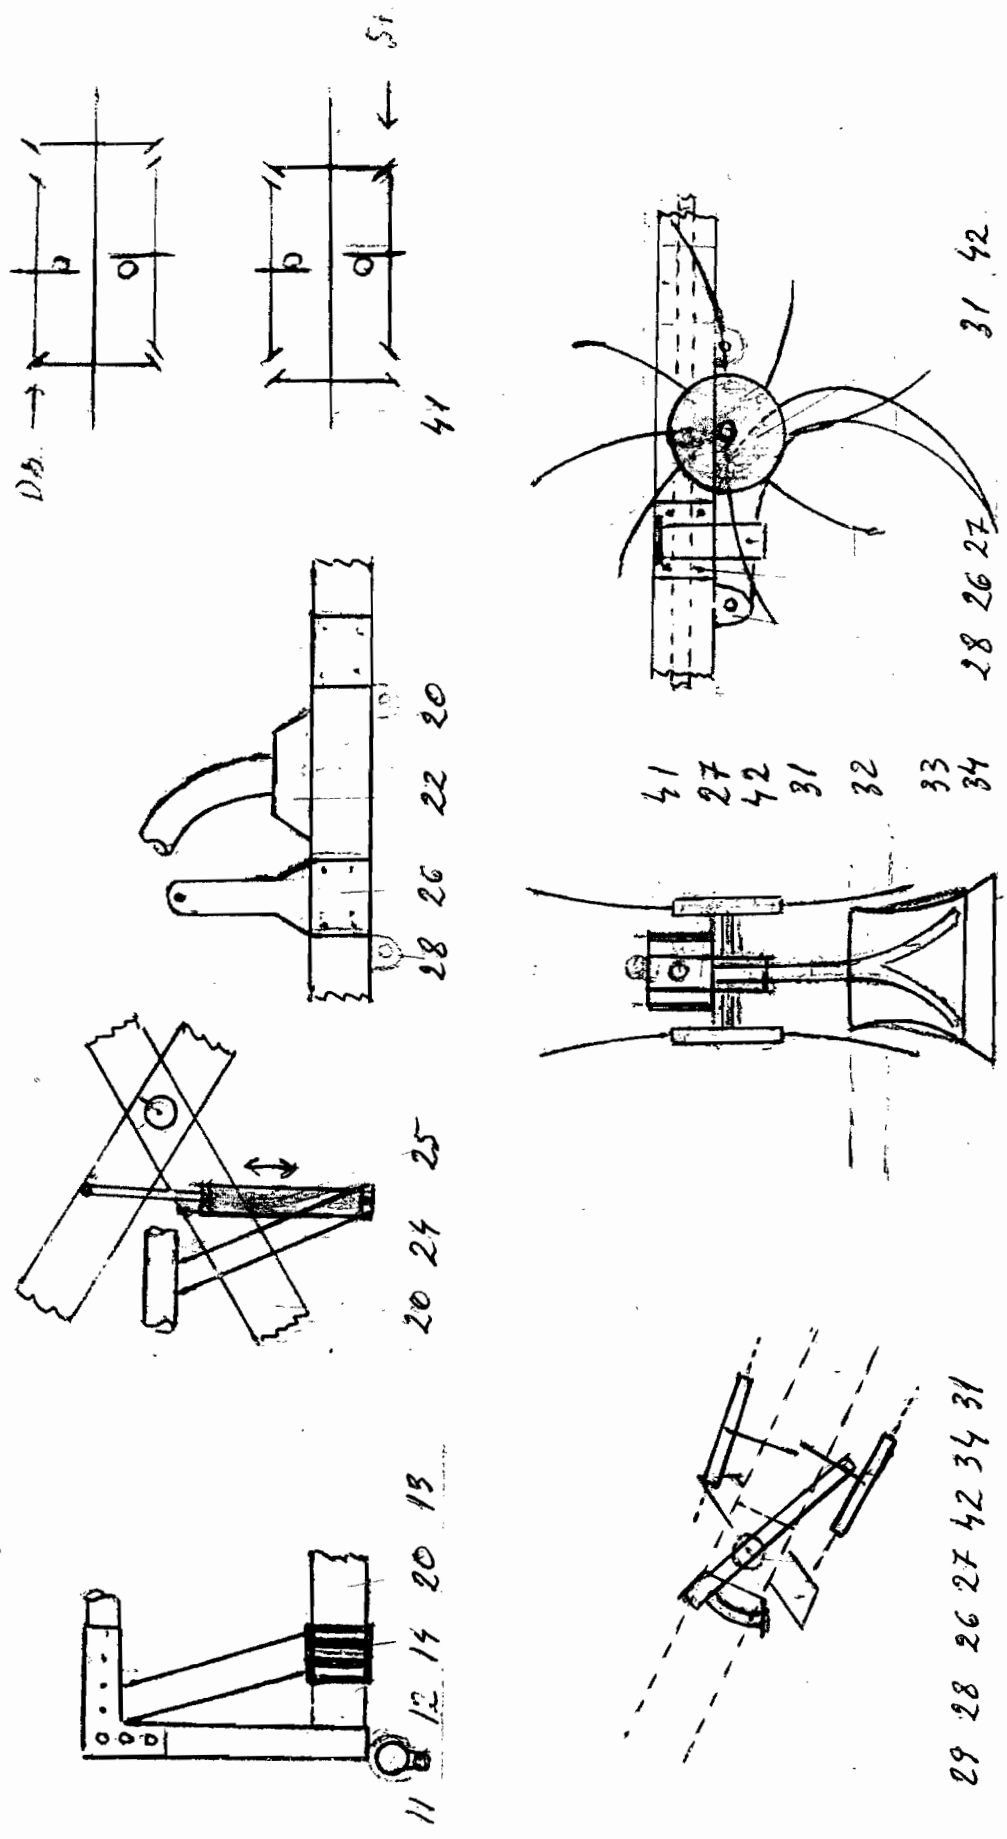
PRIVIRE IN PLAN ORIZONTAL
